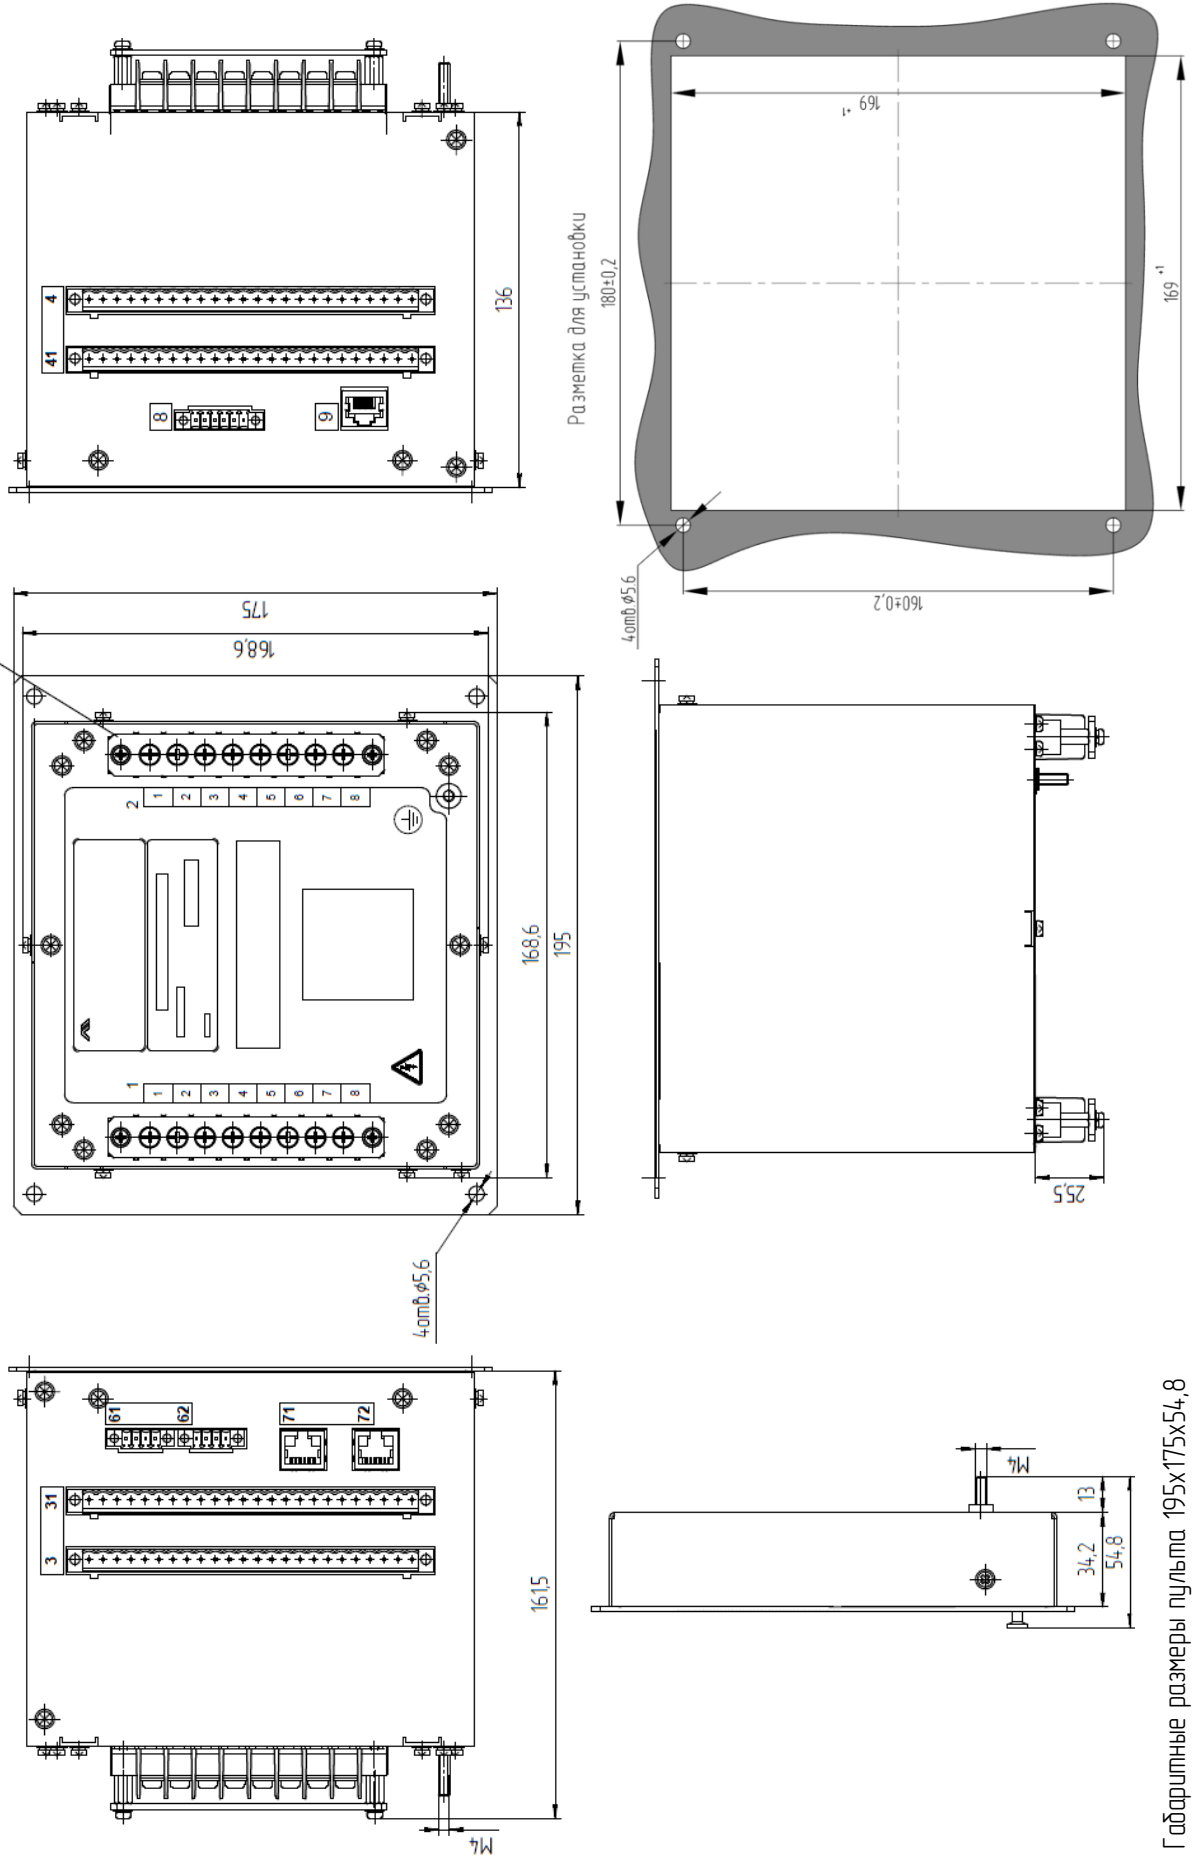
(лист 4 из 5) г) - Габаритные и установочные размеры блока ДИВГ.648228.126
